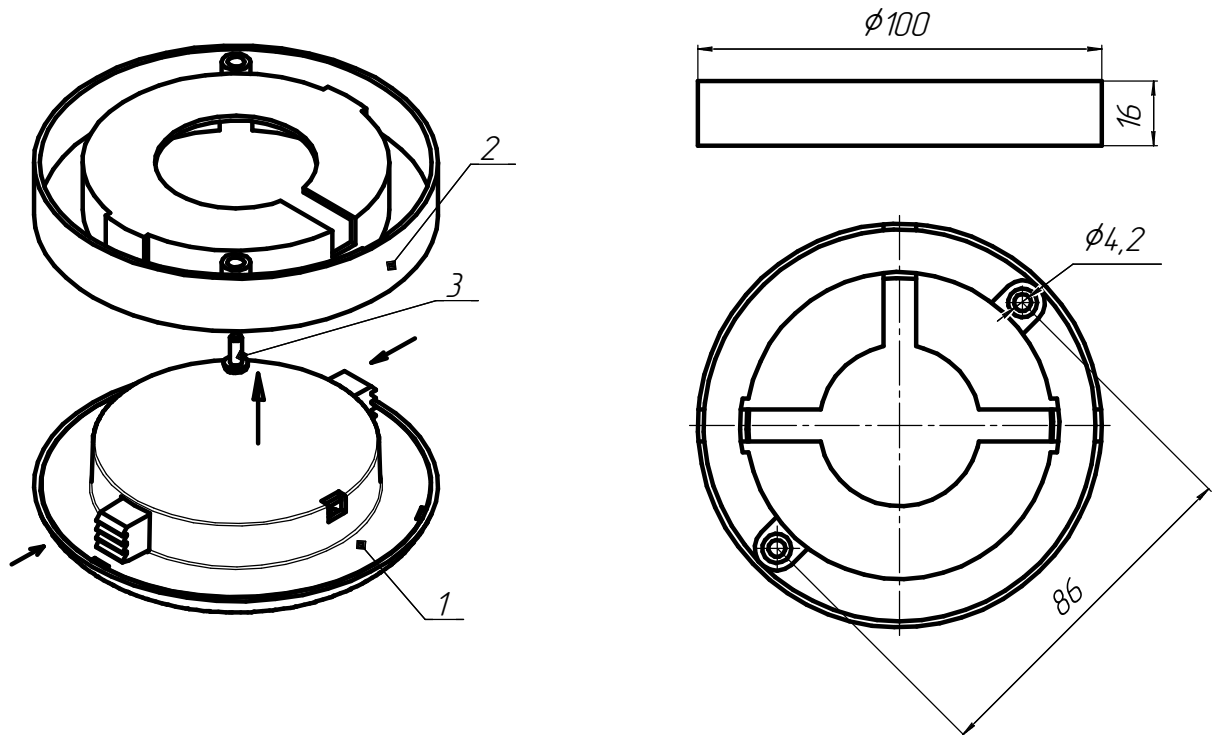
Схема монтажа светильника с монтажным кольцом;
